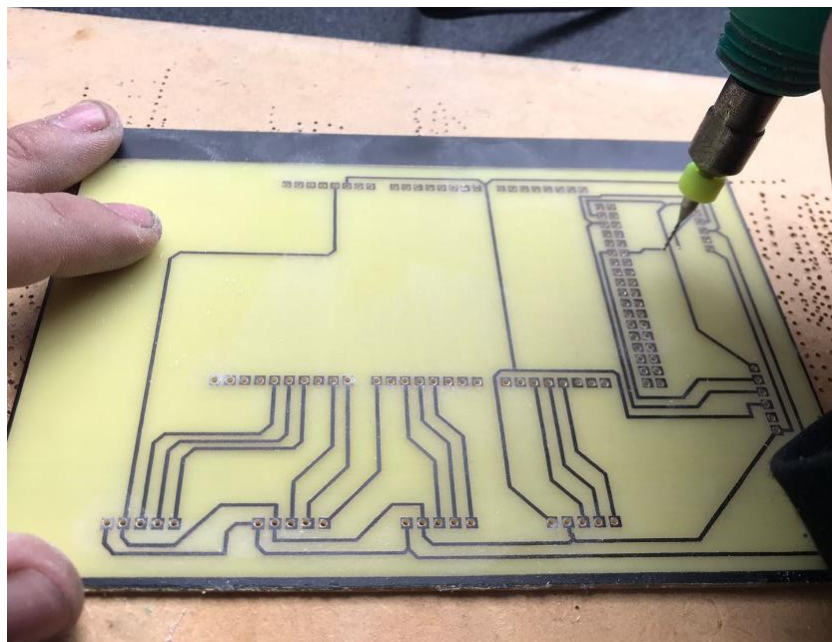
Figura VI. IV Perforación de placa PCB para soldadura de componentes
